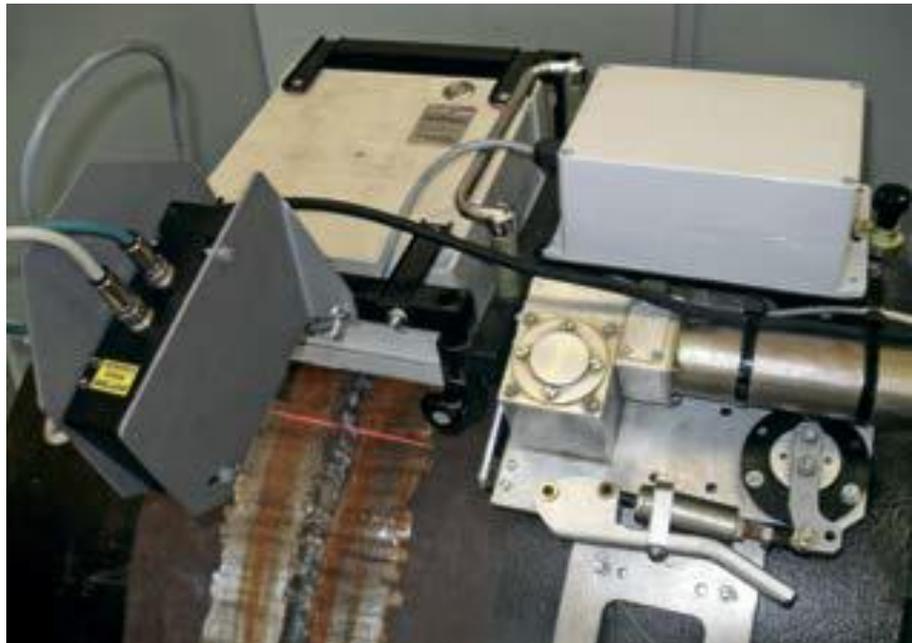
Дополнительный модуль АВИК «ВИЗИО МТ», установленный на блок детектора комплекса «УНИСКАН МТ». Время сканирования сварного соединения DN1400 – 2 мин. Параметры формы и размеров сварного соединения измеряются в соответствии с СТО Газпром 2-2.4-083–2006г.
